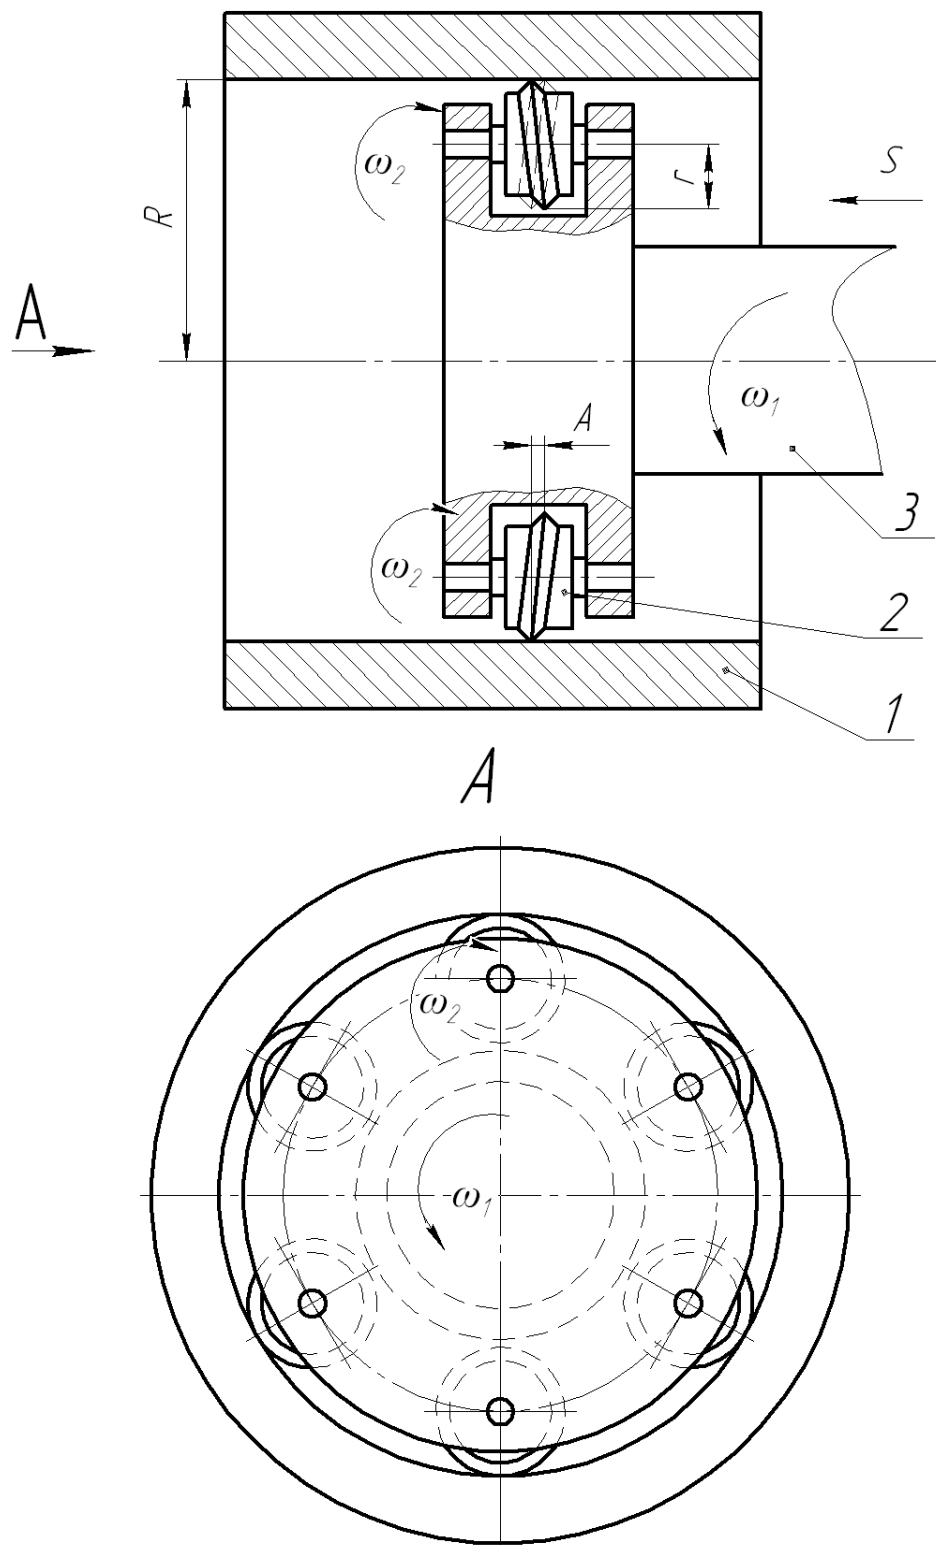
Схема процесу розкочування отворів роликми із нахиленою під кутом зовнішньою циліндричною робочою поверхнею: 1 – заготовка, 2 – ролик, 3 - оправка
